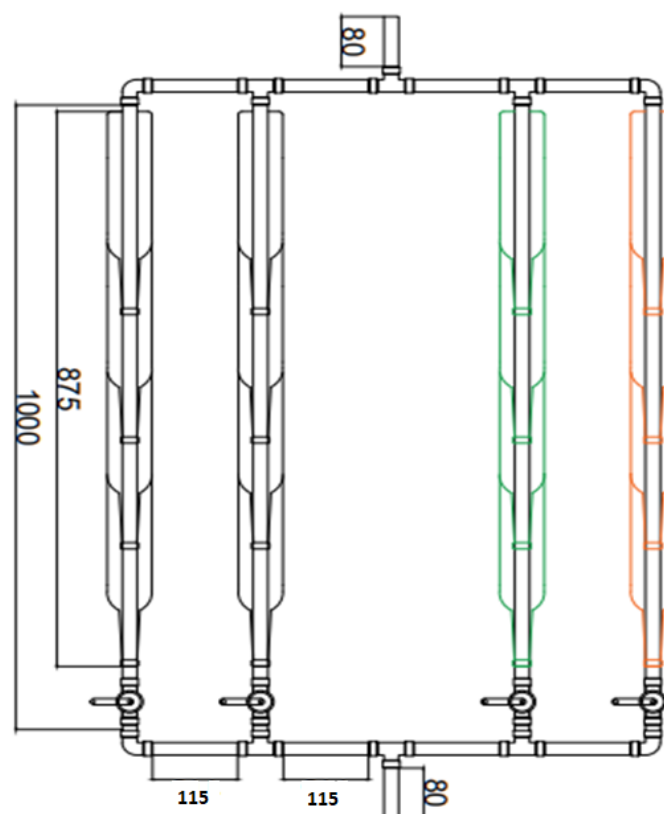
Desenho Técnico do Protótipo do Aquecedor.
